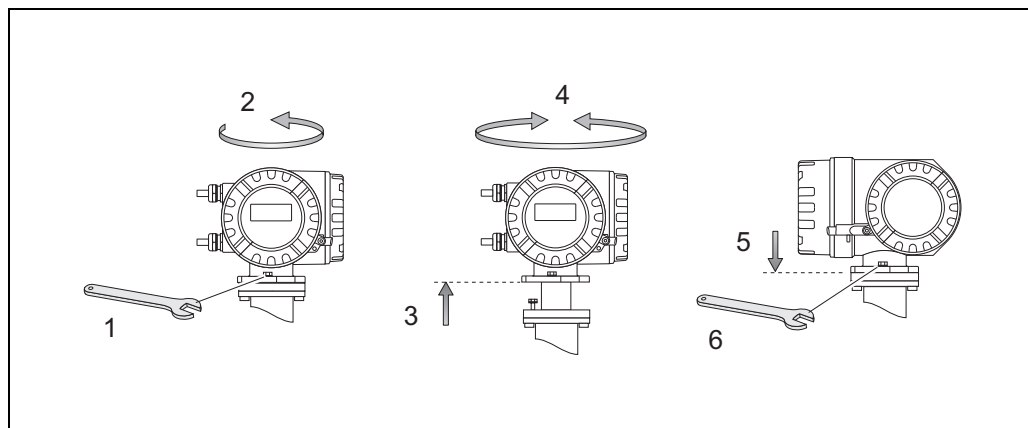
Drehen des Messumformergehäuses (Aluminium-Feldgehäuse)
